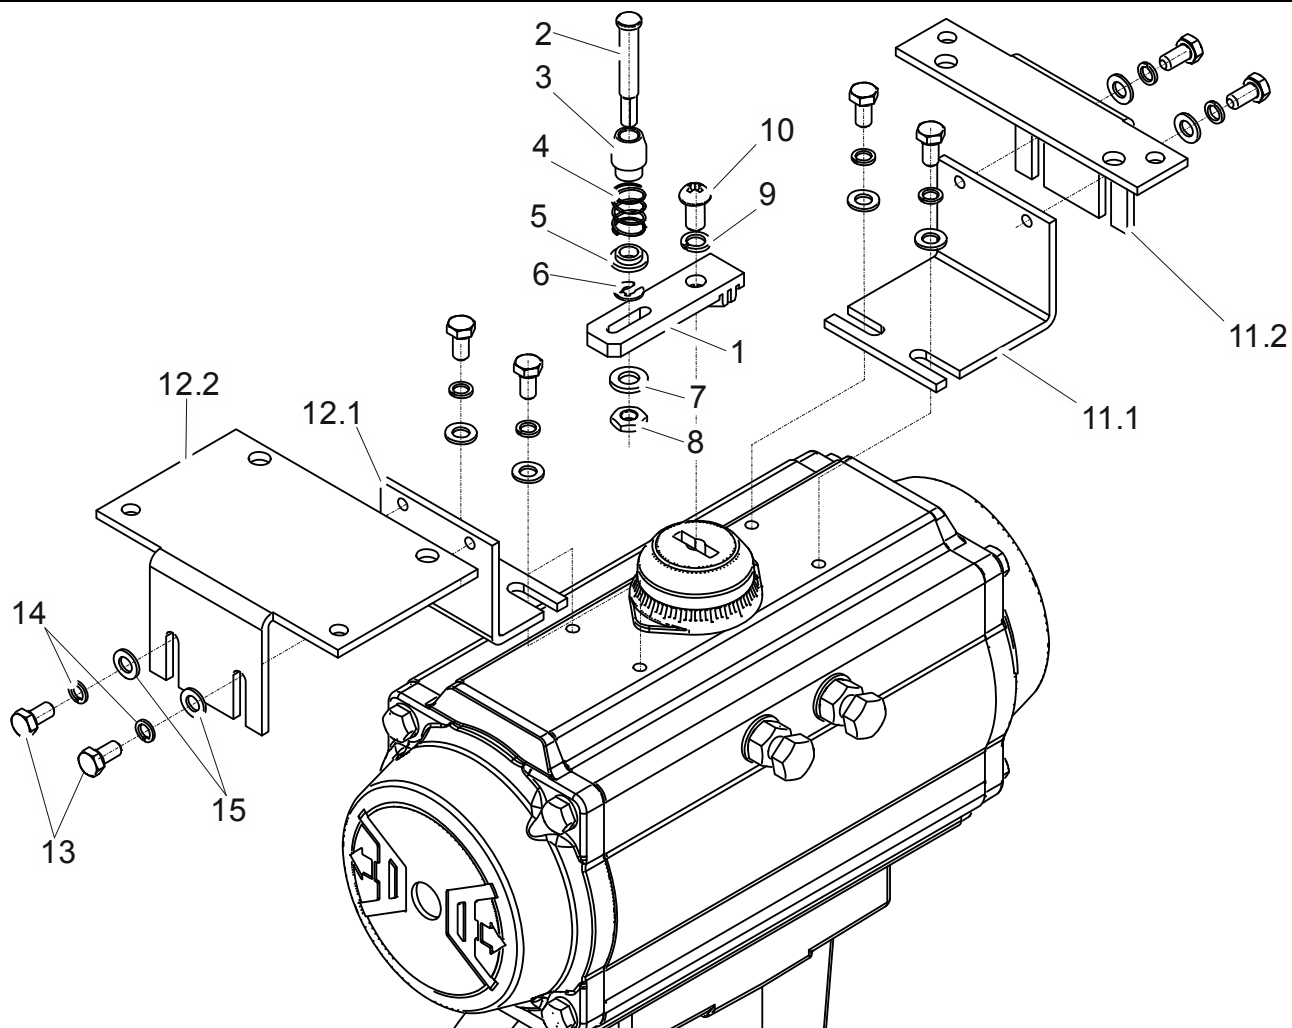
Схема установки деталей монтажного комплекта на поворотный привод
